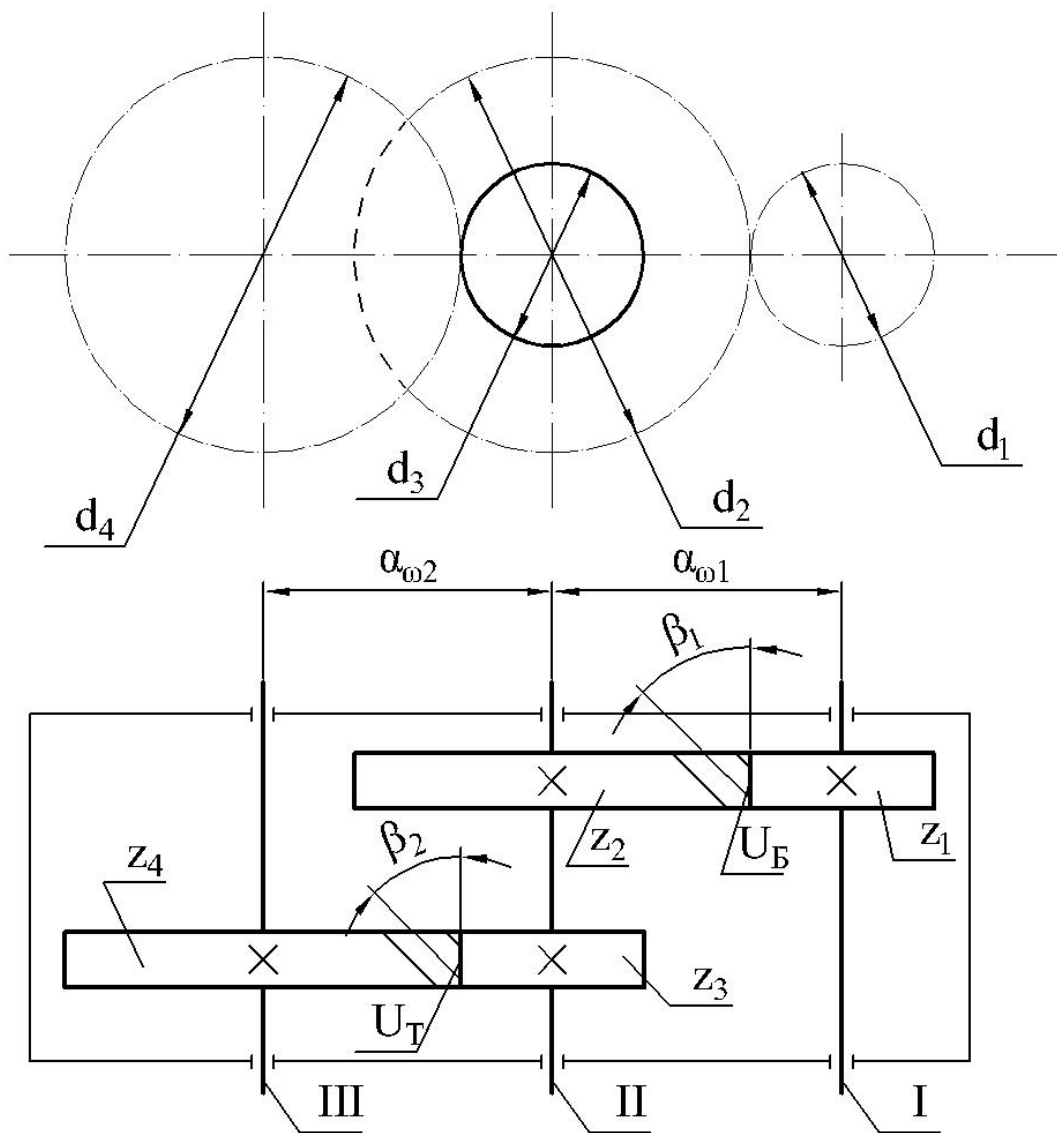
Кинематическая схема двухступенчатого редуктора:
